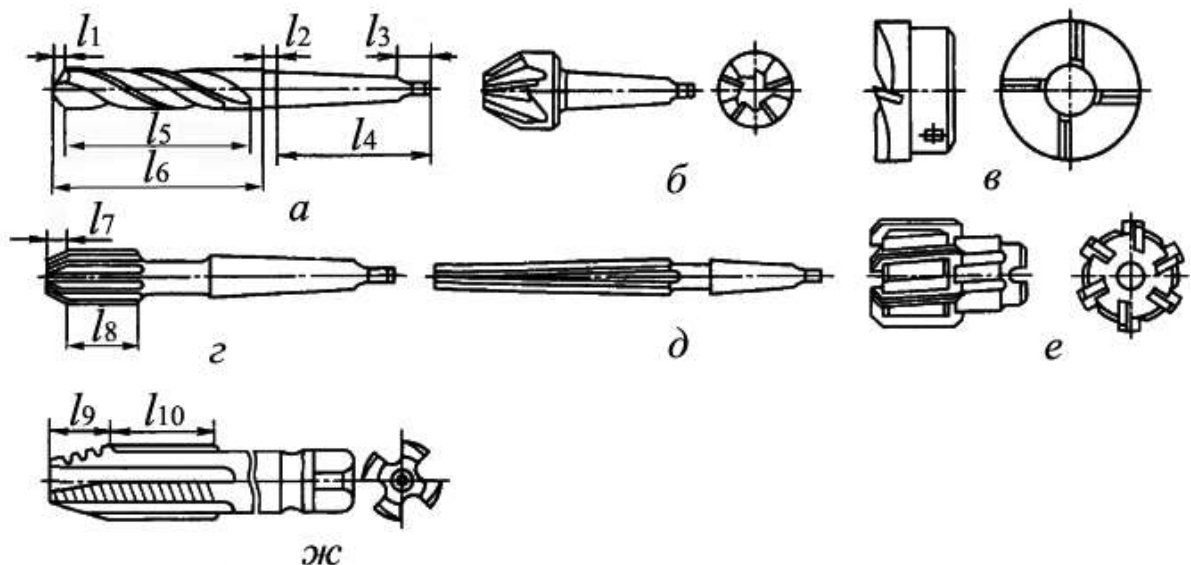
Інструменти для обробки отворів на свердлильних верстатах
